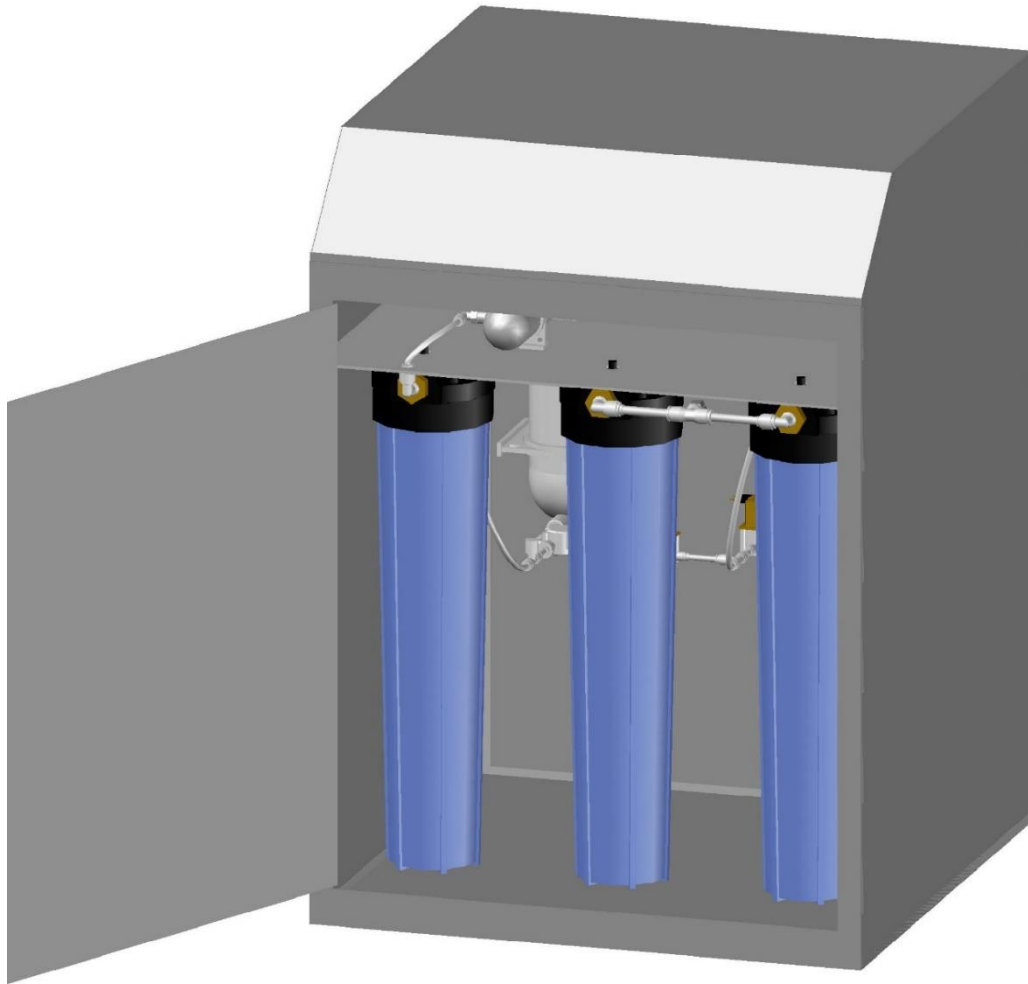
Diseño acceso rápido a los filtros de la planta.
